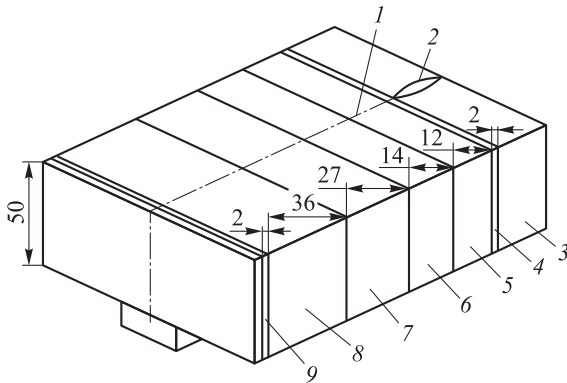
Общий вид заготовки из сплава ВТ23 с указанием габаритов раскроя на образцы для исследования дефектов и микроструктуры: 1 — шов; 2 — технологический кратер; 3 — образец № 1; 4 — образец № 2; 5 — образец № 3; 6 — образец № 4; 7 — образец № 5; 8 — образец № 6; 9 — образец № 7
